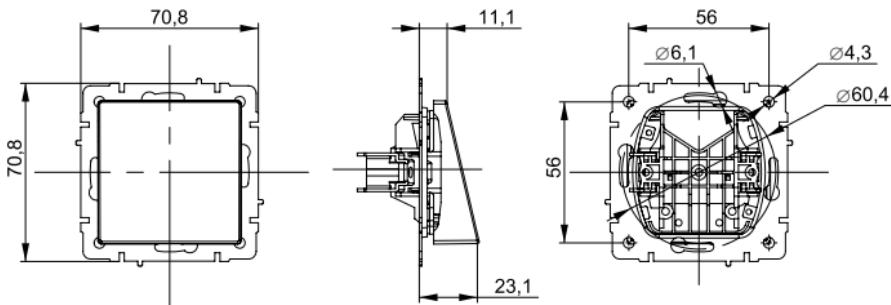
Габаритные и установочные размеры вывода кабеля / Figure 1 – Overall and installation dimensions of the
